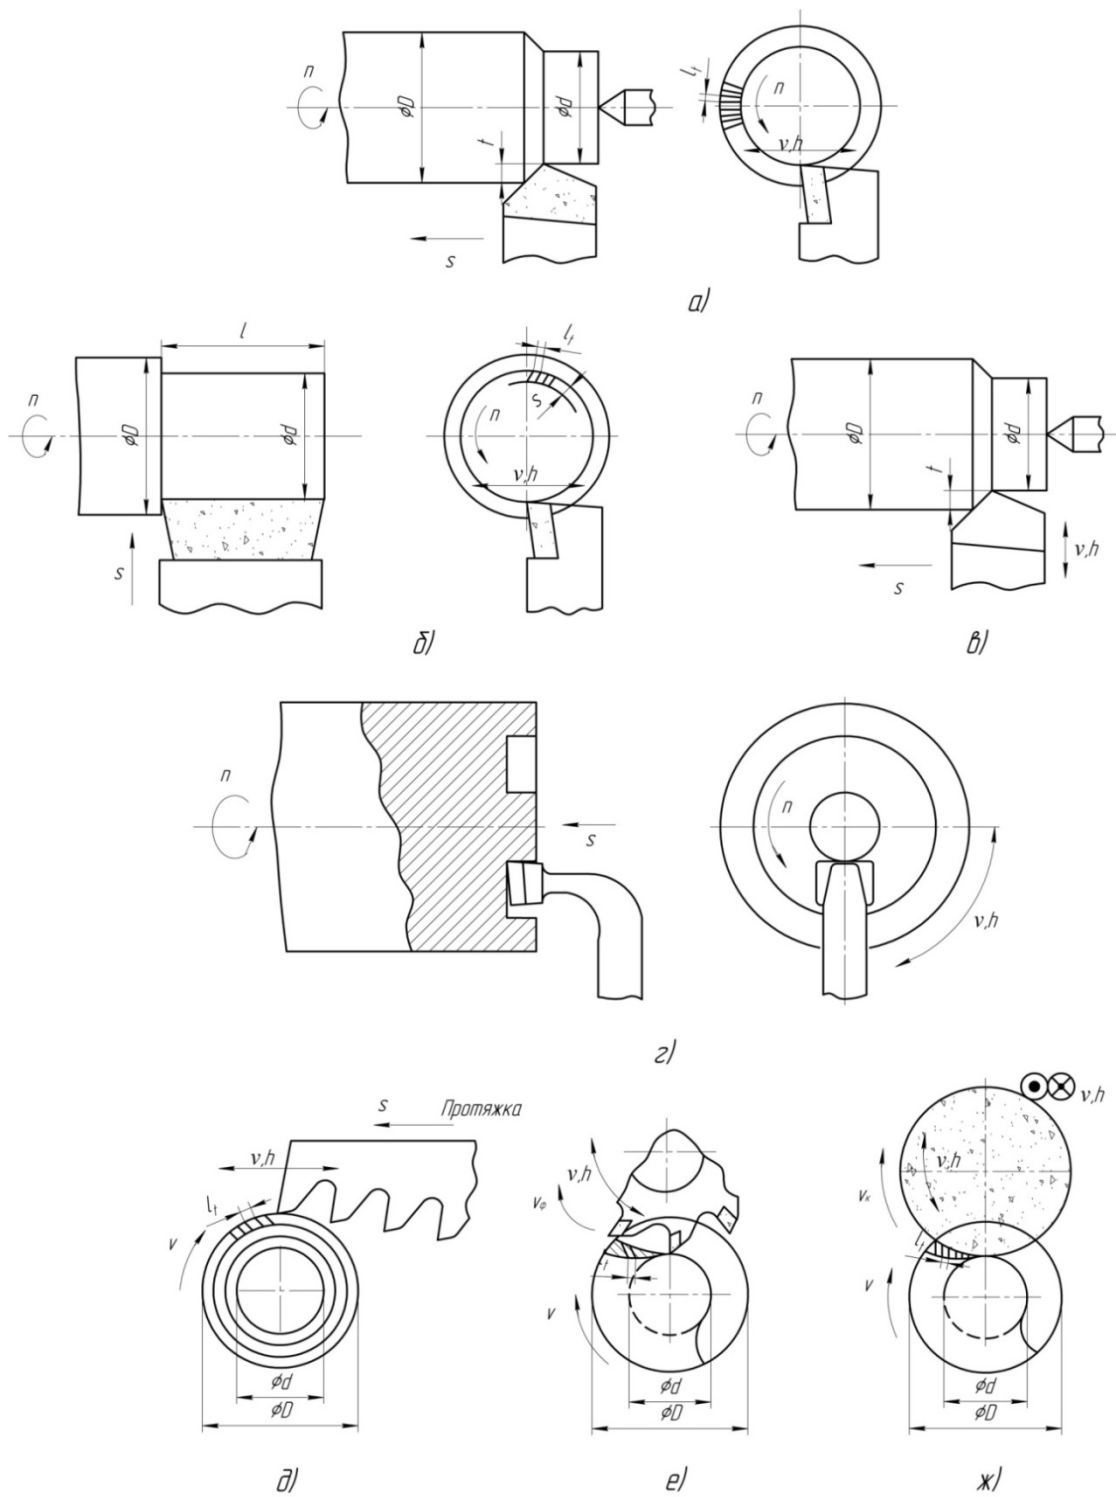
Схеми способів обробки вібраційним різанням циліндричних поверхнь (v, h – напрям вібрацій інструмента; v – напрям колової швидкості деталі; s – подача; n – частота обертання деталі)
